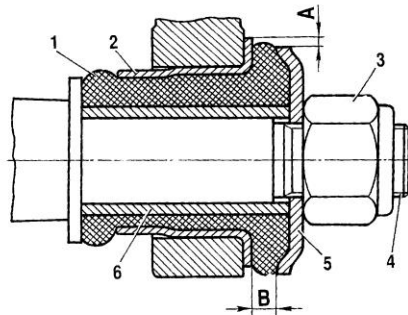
Перевірка стану резинометалевого шарніра важеля передньої підвіски
